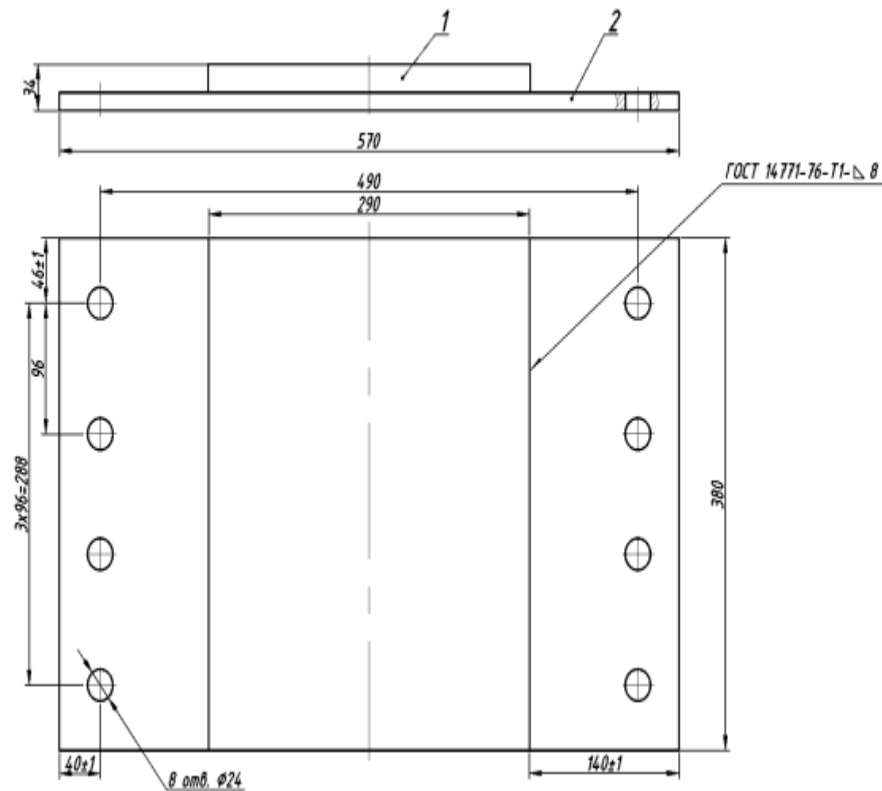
Креслення планки автозчепи: 1, 2 – приварочна та опорна пластина
